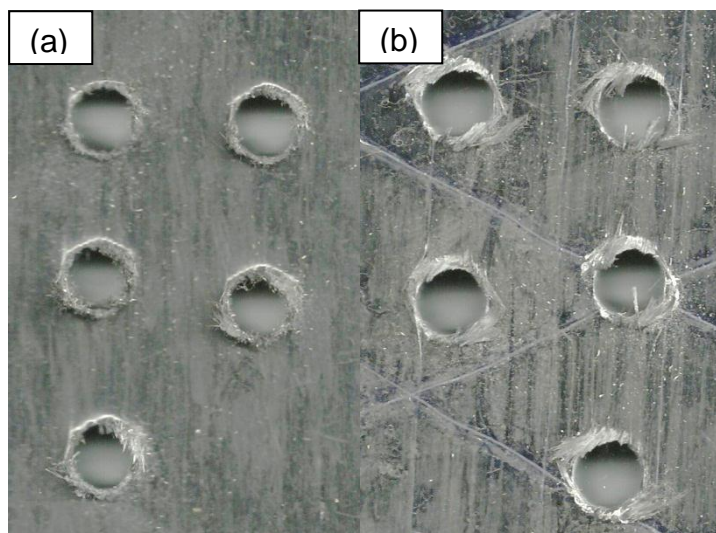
Furações realizadas com a broca helicoidal: (a) Superfície de entrada; (b) Superfície de saída.
